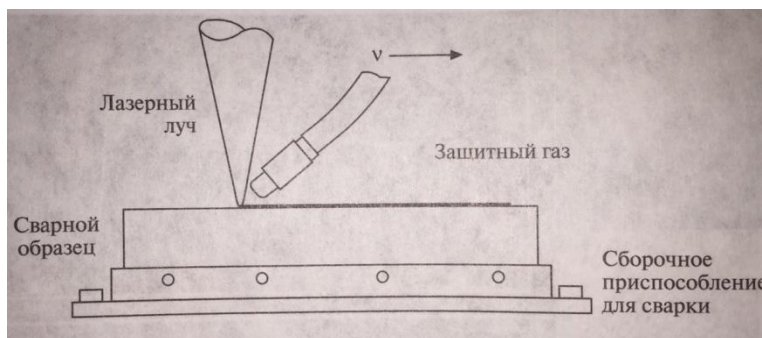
Схема лазерной сварки, защитный газ предотвращает окисление поверхности в процессе сварки
